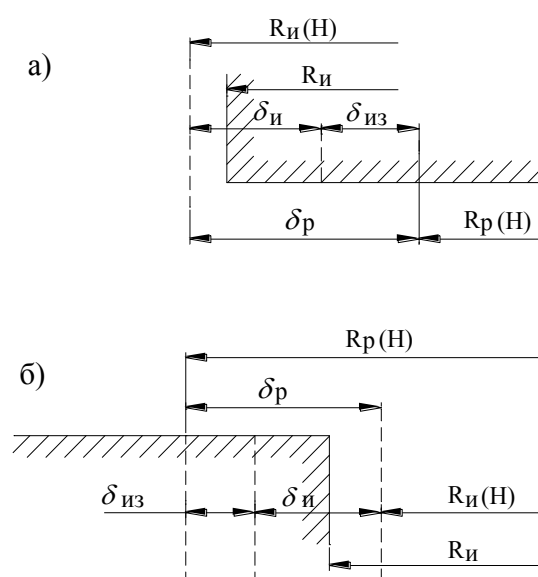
Схема расположения полей допусков для разделительных операций:
